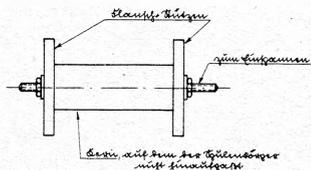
Die Wickelvorrichtung für die Spule (2 Holzscheiben als Flanschstützen, 1 Holzkern, 1 Gewindestange zum Zusammenhalten).
